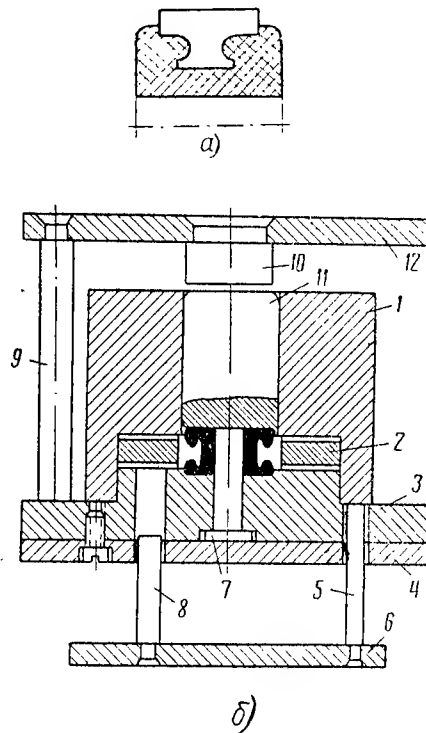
Коллектор на пластмассе: а — конструкция коллектора, б — пресс-форма
